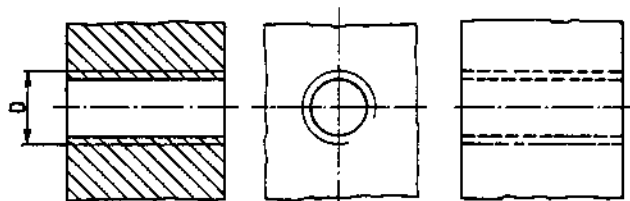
Per le filettature in sezione la cresta e il fondo del filetto devono essere rappresentati con lo stesso criterio precisato per le filettature in vista. Il tratteggio di sezione deve terminare sulla linea indicante la cresta del filetto.
